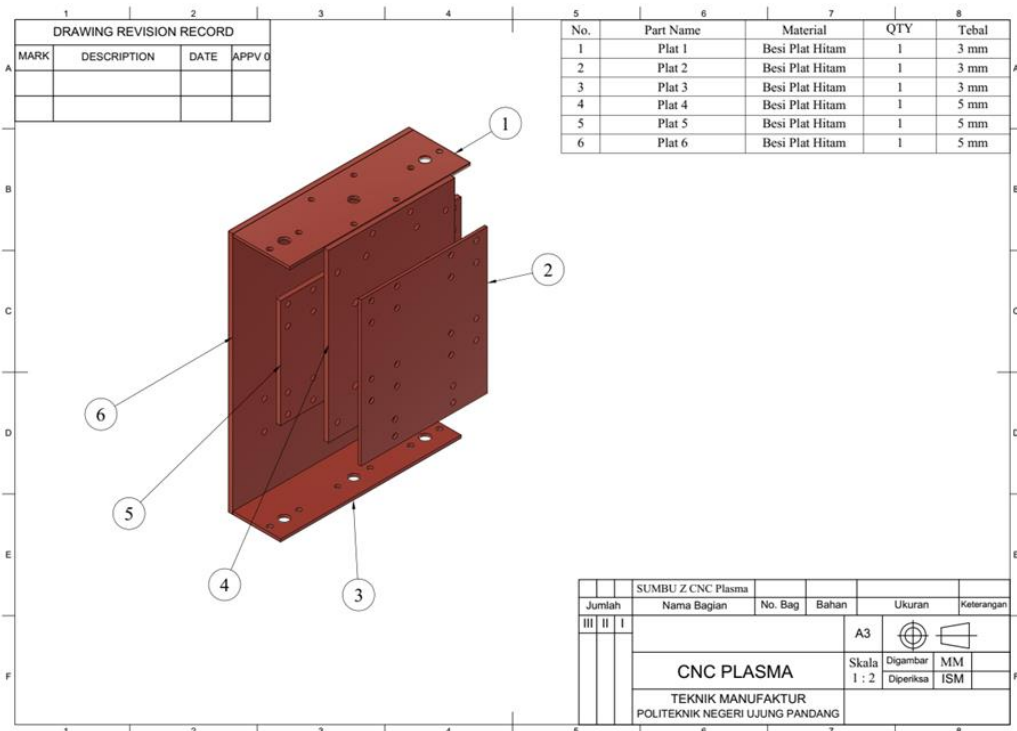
Desain pemegang torch pada mesin CNC Plasma
